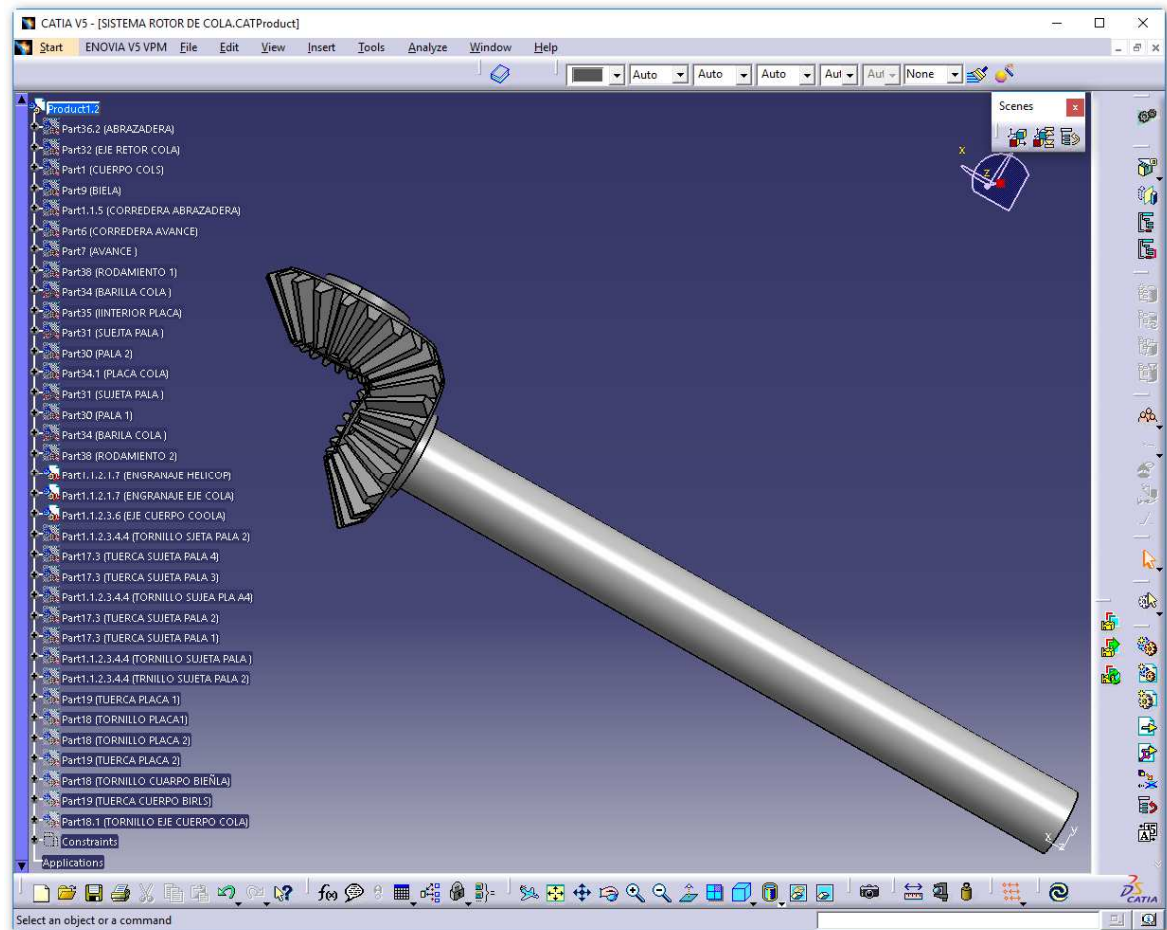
Mecanismo de transmisión del rotor de cola.
